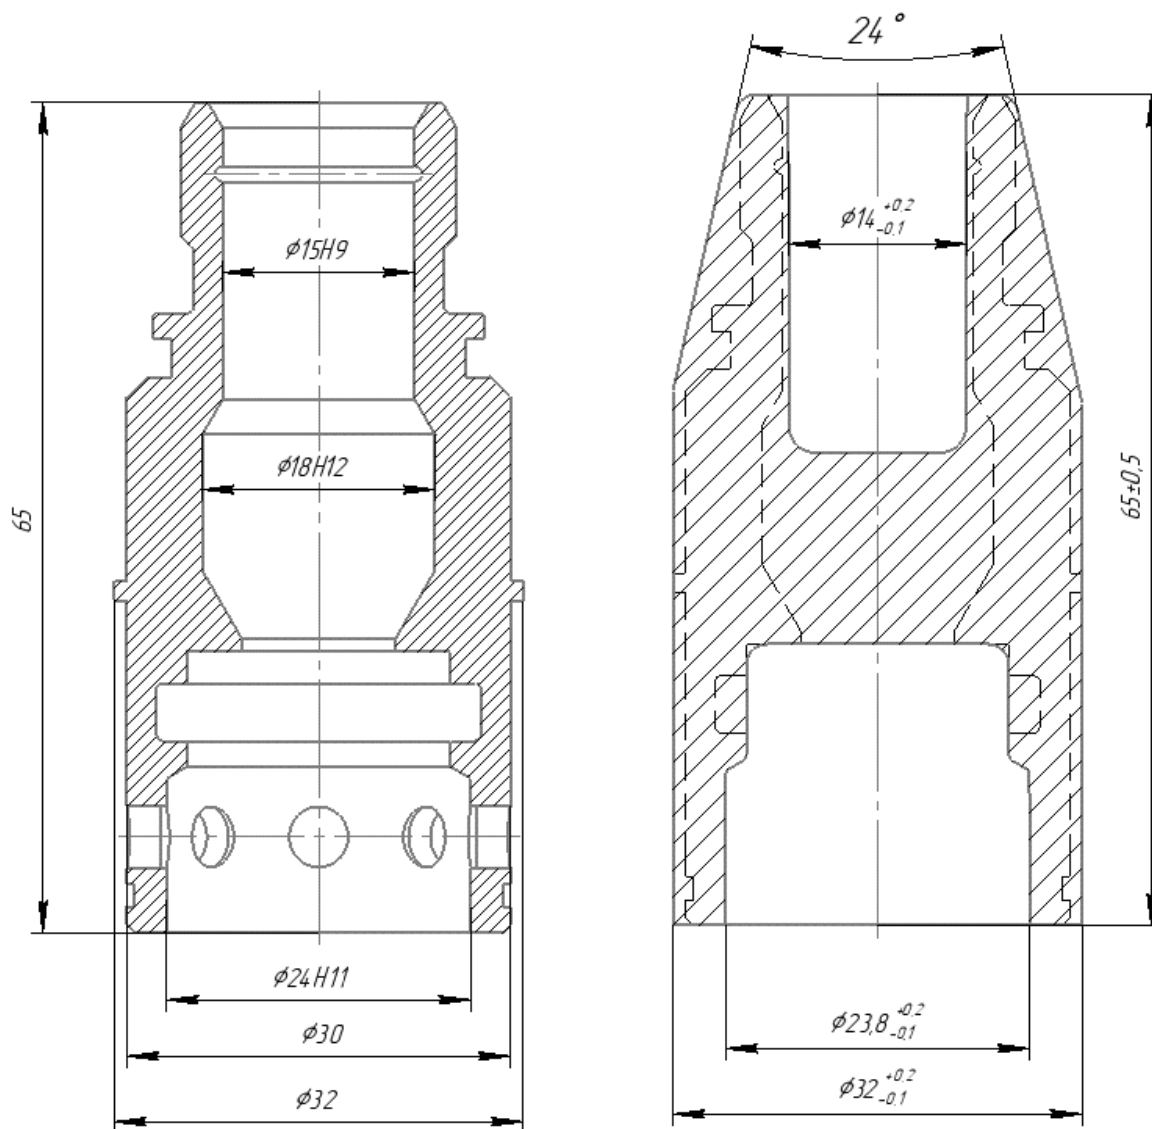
Эскиз детали гидромуфты «Корпус левый»: а – деталь; б – поковка
